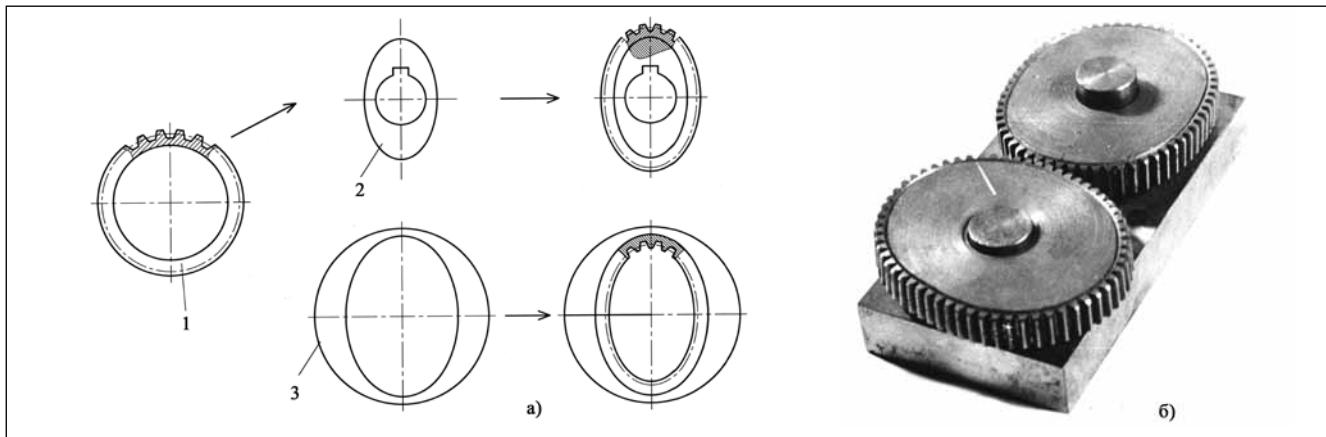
Некруглые зубчатые колёса: а) способ изготовления, б) зацепление овальных зубчатых колёс. 1 — круглый зубчатый венец, 2 — некруглый обод наружного колеса, 3 — некруглый обод внутреннего колеса
